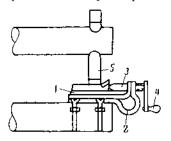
Схема пагрева для пайки твердосплавных резцов на точечной сварочной машине:
